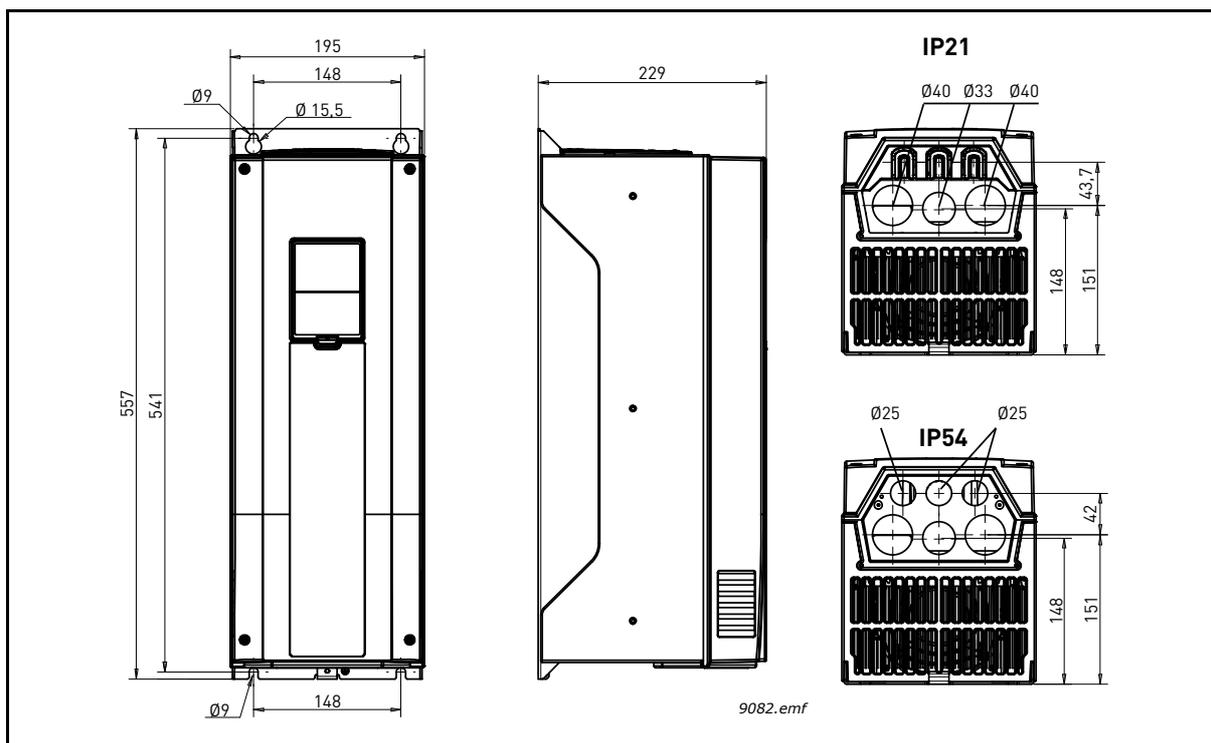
Dimensiones del variador de CA Vacon, MR6, montaje para la pared
